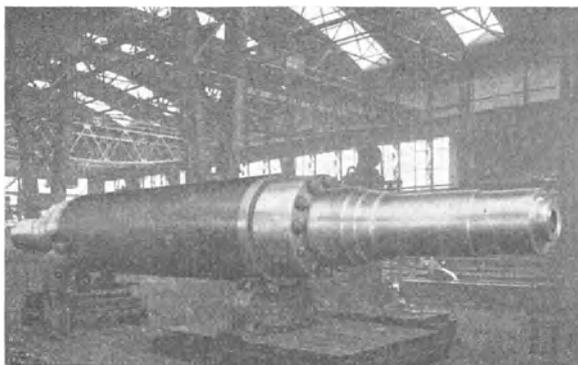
3teiliger schwerer Rotorkörper auf Rollenuntersätzen.
